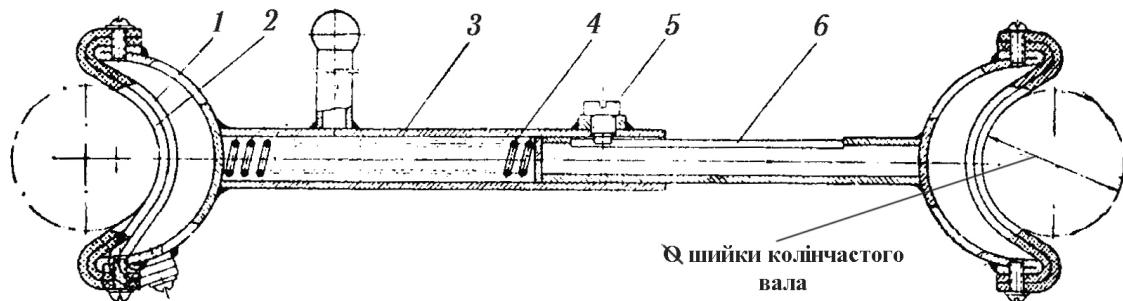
Хомут у зборі до верстата для полірування шийок колінчастих валів: 1 - стрічка шкіряна; 2 - стрічка фетрова; 3 - хомут; 4 - пружина; 5 - гвинт; 6- хомут.
